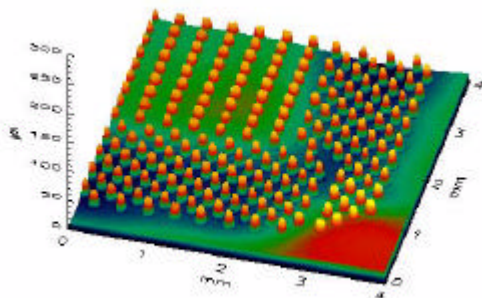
Halbleiter Bauelement mit BGA (Ball Grid Array)
